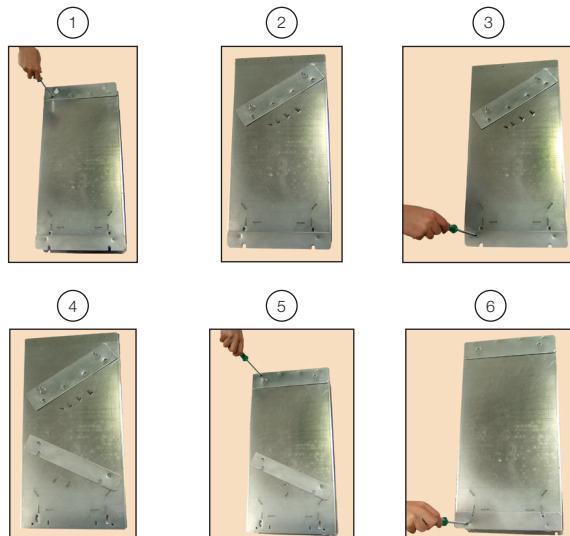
Reposite os suportes de montagem nas mecânicas A a E. Nas mecânicas F e G os suportes devem ser removidos
